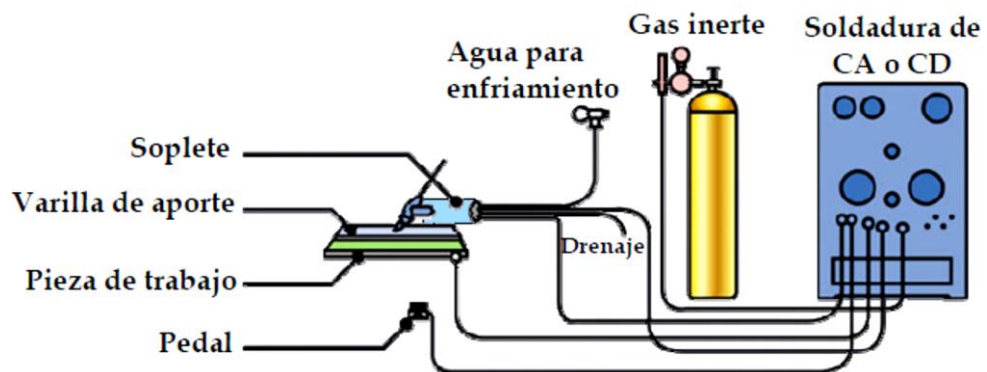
Equipo de soldadura por arco de tungsteno y gas
